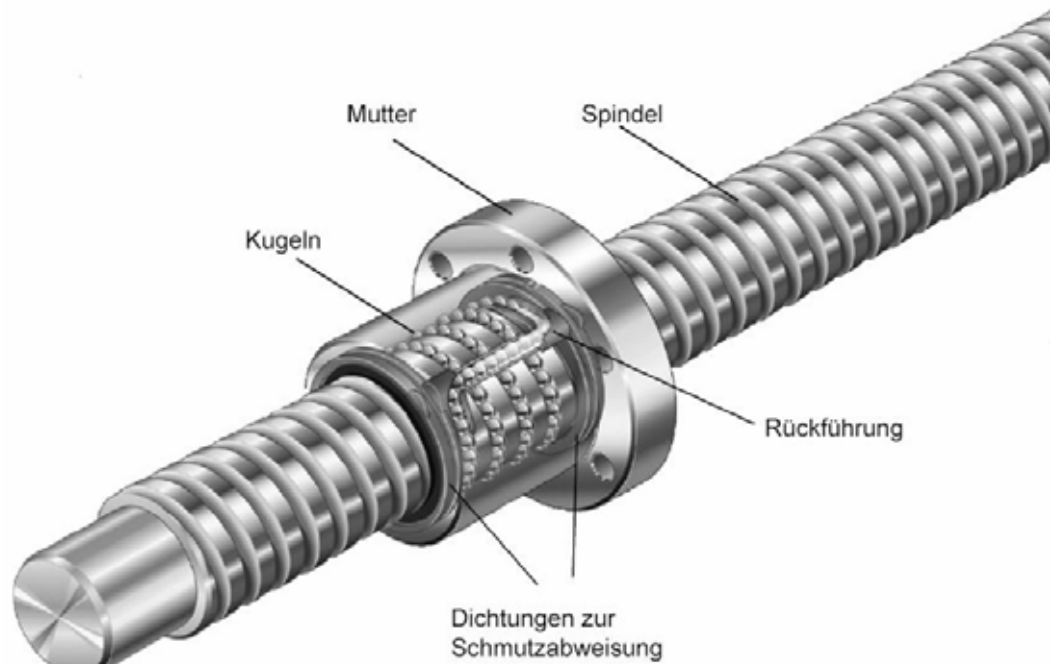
Kugelrollspindel mit Kugelführung Quelle: INA-FAG
